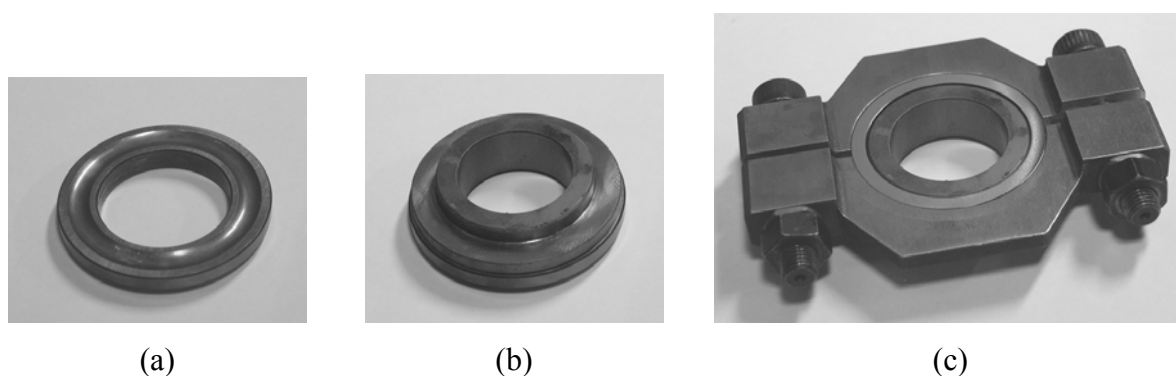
Etapas da montagem do corpo-de-prova com tensionador: pista inferior (a); pista e bucha de acoplamento (b); conjunto corpo-de-prova/bucha/pista montado (c).
